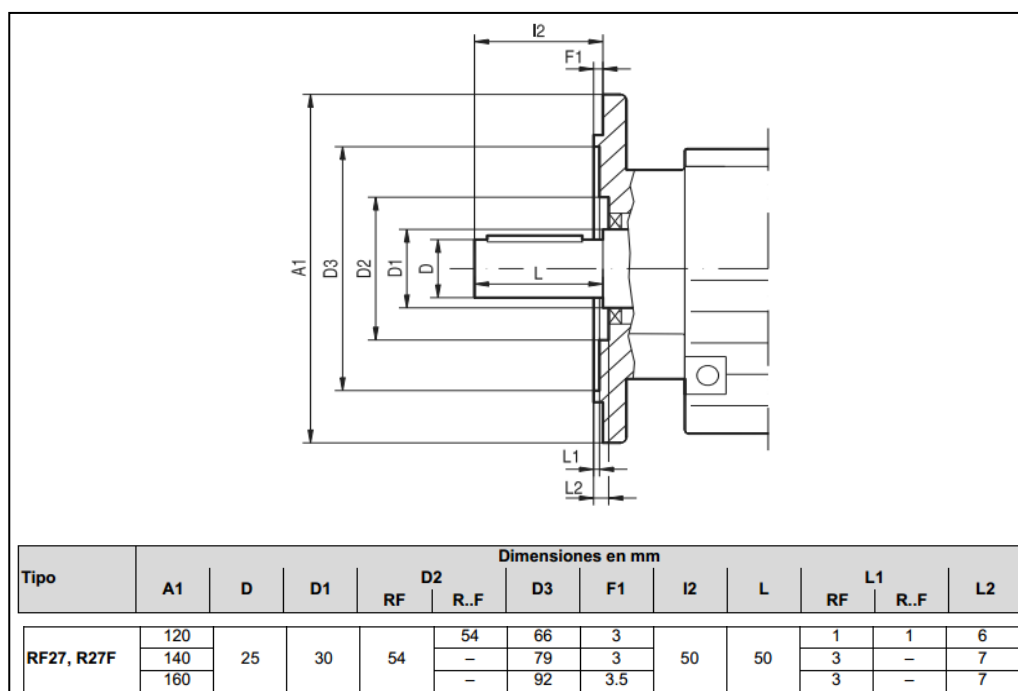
Dimensiones motor línea RF7, versión con brida B5
